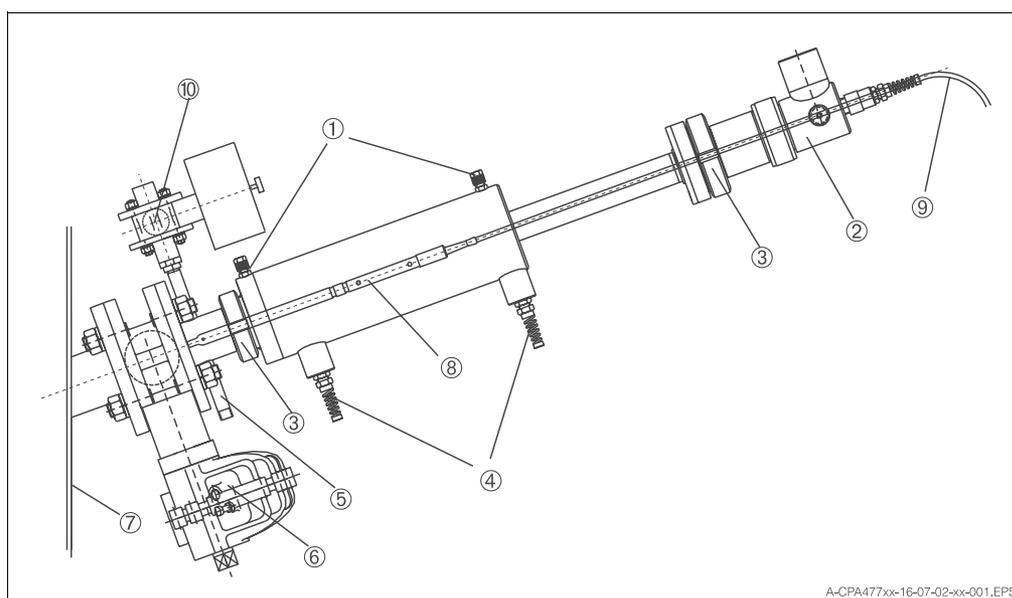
Armatura retrattile CleanFit P CPA 477 in posizione di manutenzione
